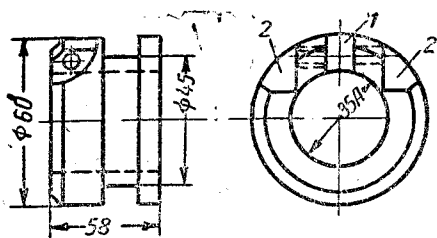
Приспособление для фрезерования муфты по новому технологическому процессу:
